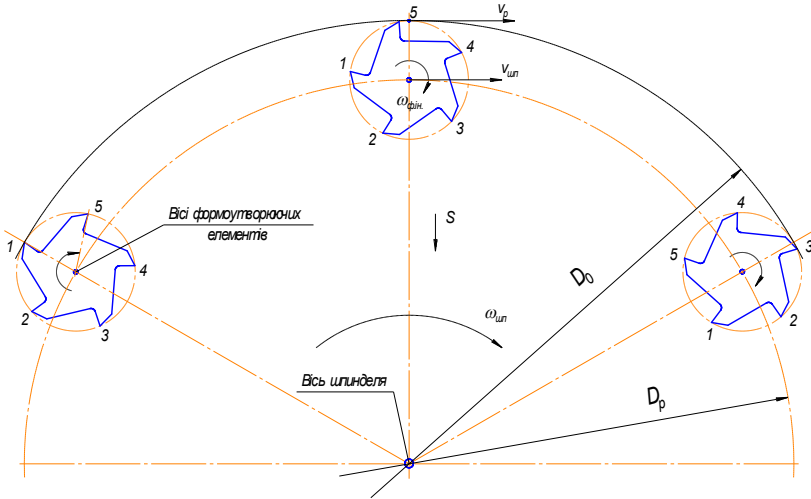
Схема торцевого інструмента з двома обертальними головними рухами
